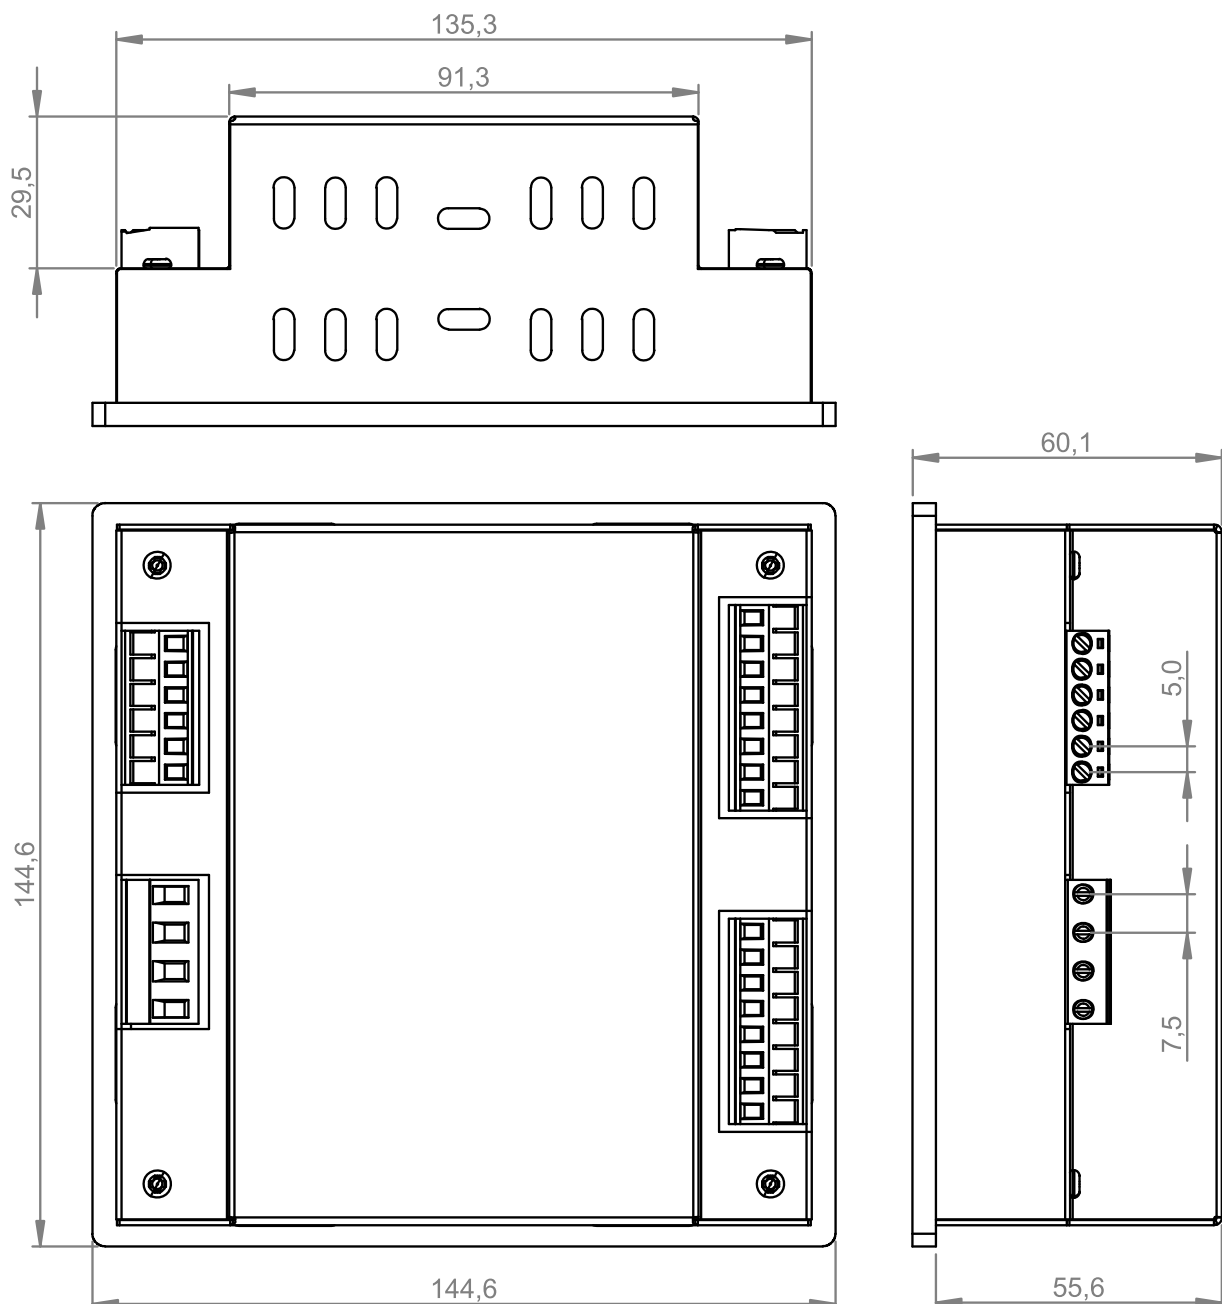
Dimensiones del controlador PFWD01 en milímetros
